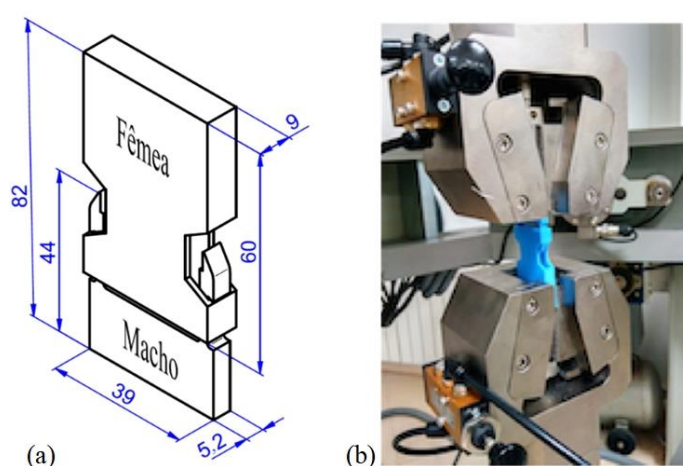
Sistema *snap-fit* (dimensões em mm) (a) e (b) ensaio de tração (adaptado de CHACÓN *et al.*, 2017).
